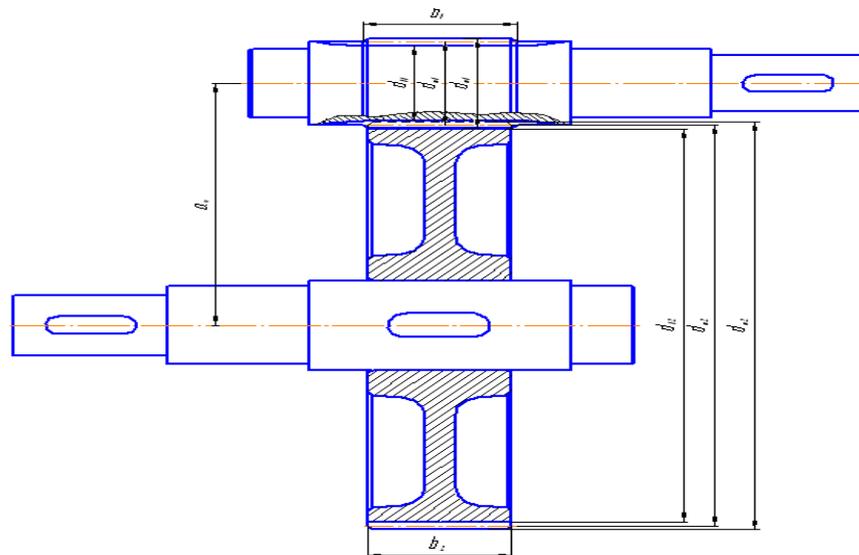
Схема к расчёту цилиндрической зубчатой передачи
